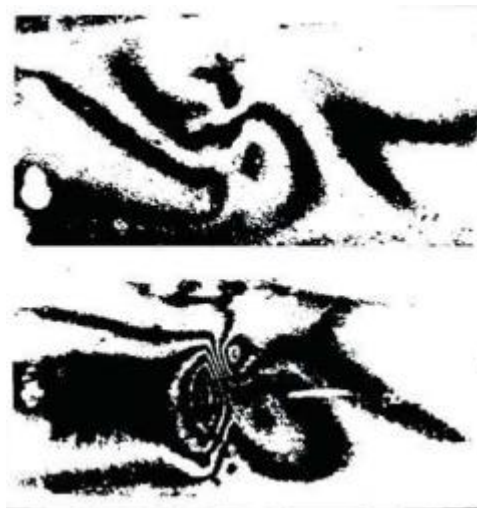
Análisis de defectos en la soldadura de tubos de acero. Soldadura correcta (imagen superior) y mala soldadura (imagen inferior) [7]
